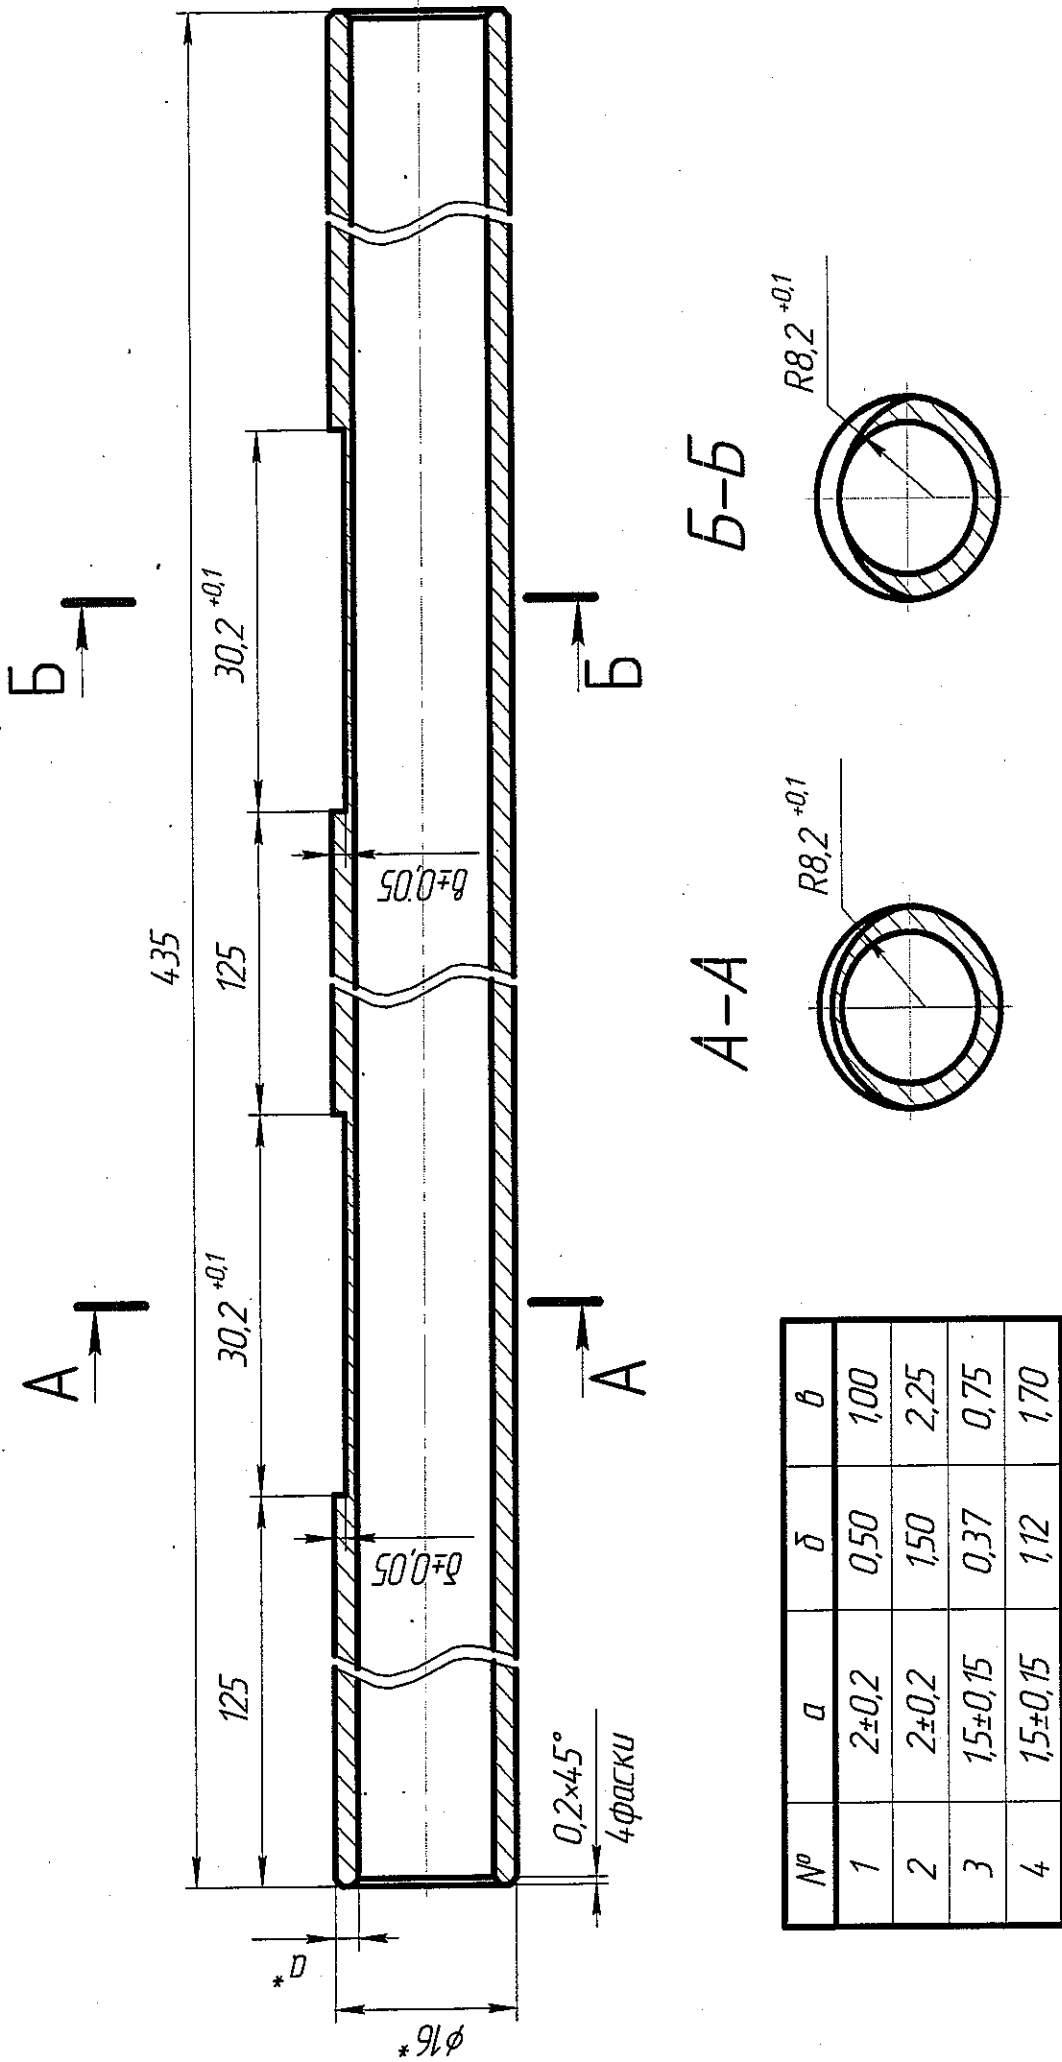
Образец теплообменной трубы ПГ с поперечными локальными дефектами типа "трещина"
